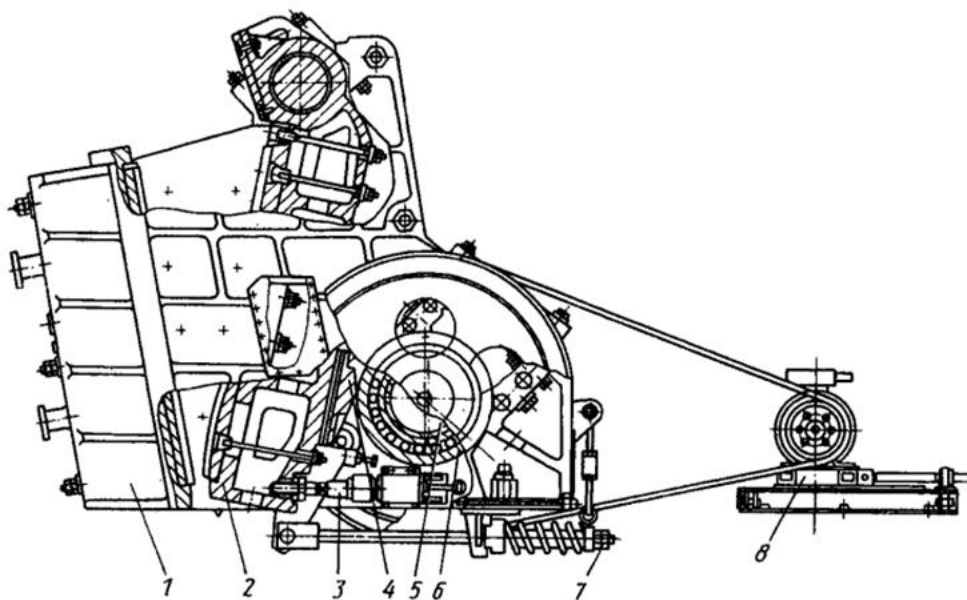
Щокова дробарка СМД-184 з роликом:
